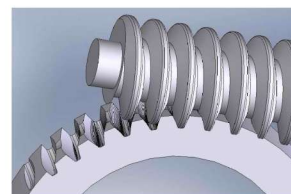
Модель червяка и заготовки червячного колеса в рабочем положении
